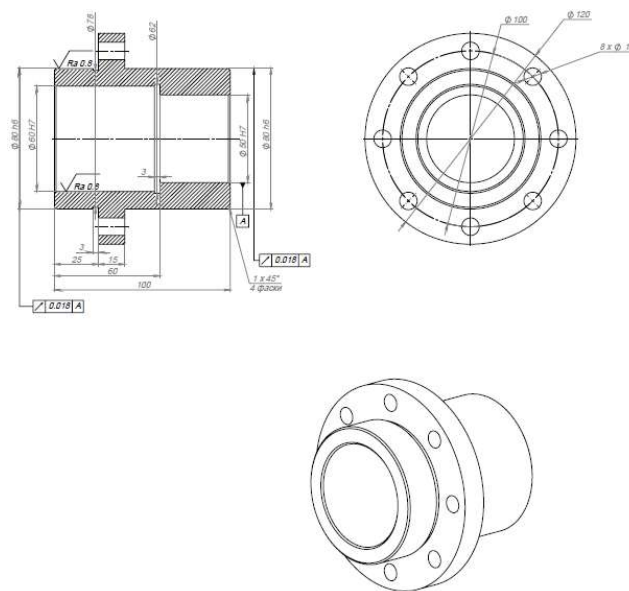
Креслення деталі «Ступиця SK-15.80.50»
